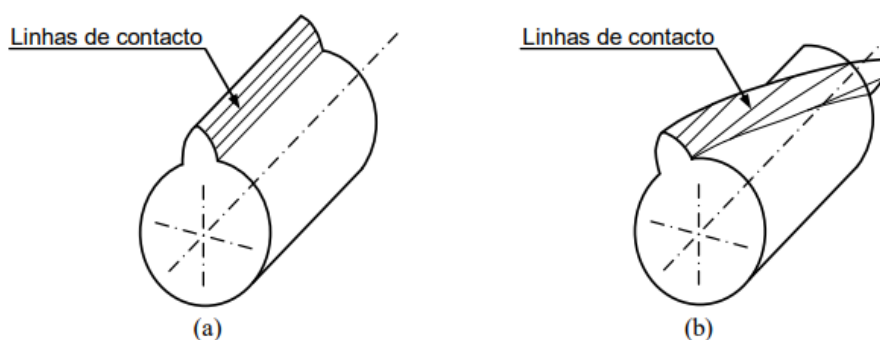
Linhas de engrenamento em engrenagem cilíndrica de a) dentado reto; b) dentado helicoidal [26]
